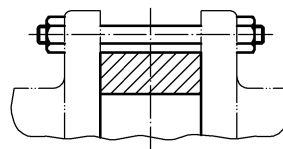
Gehäuse zum Einklemmen ohne Flansch
